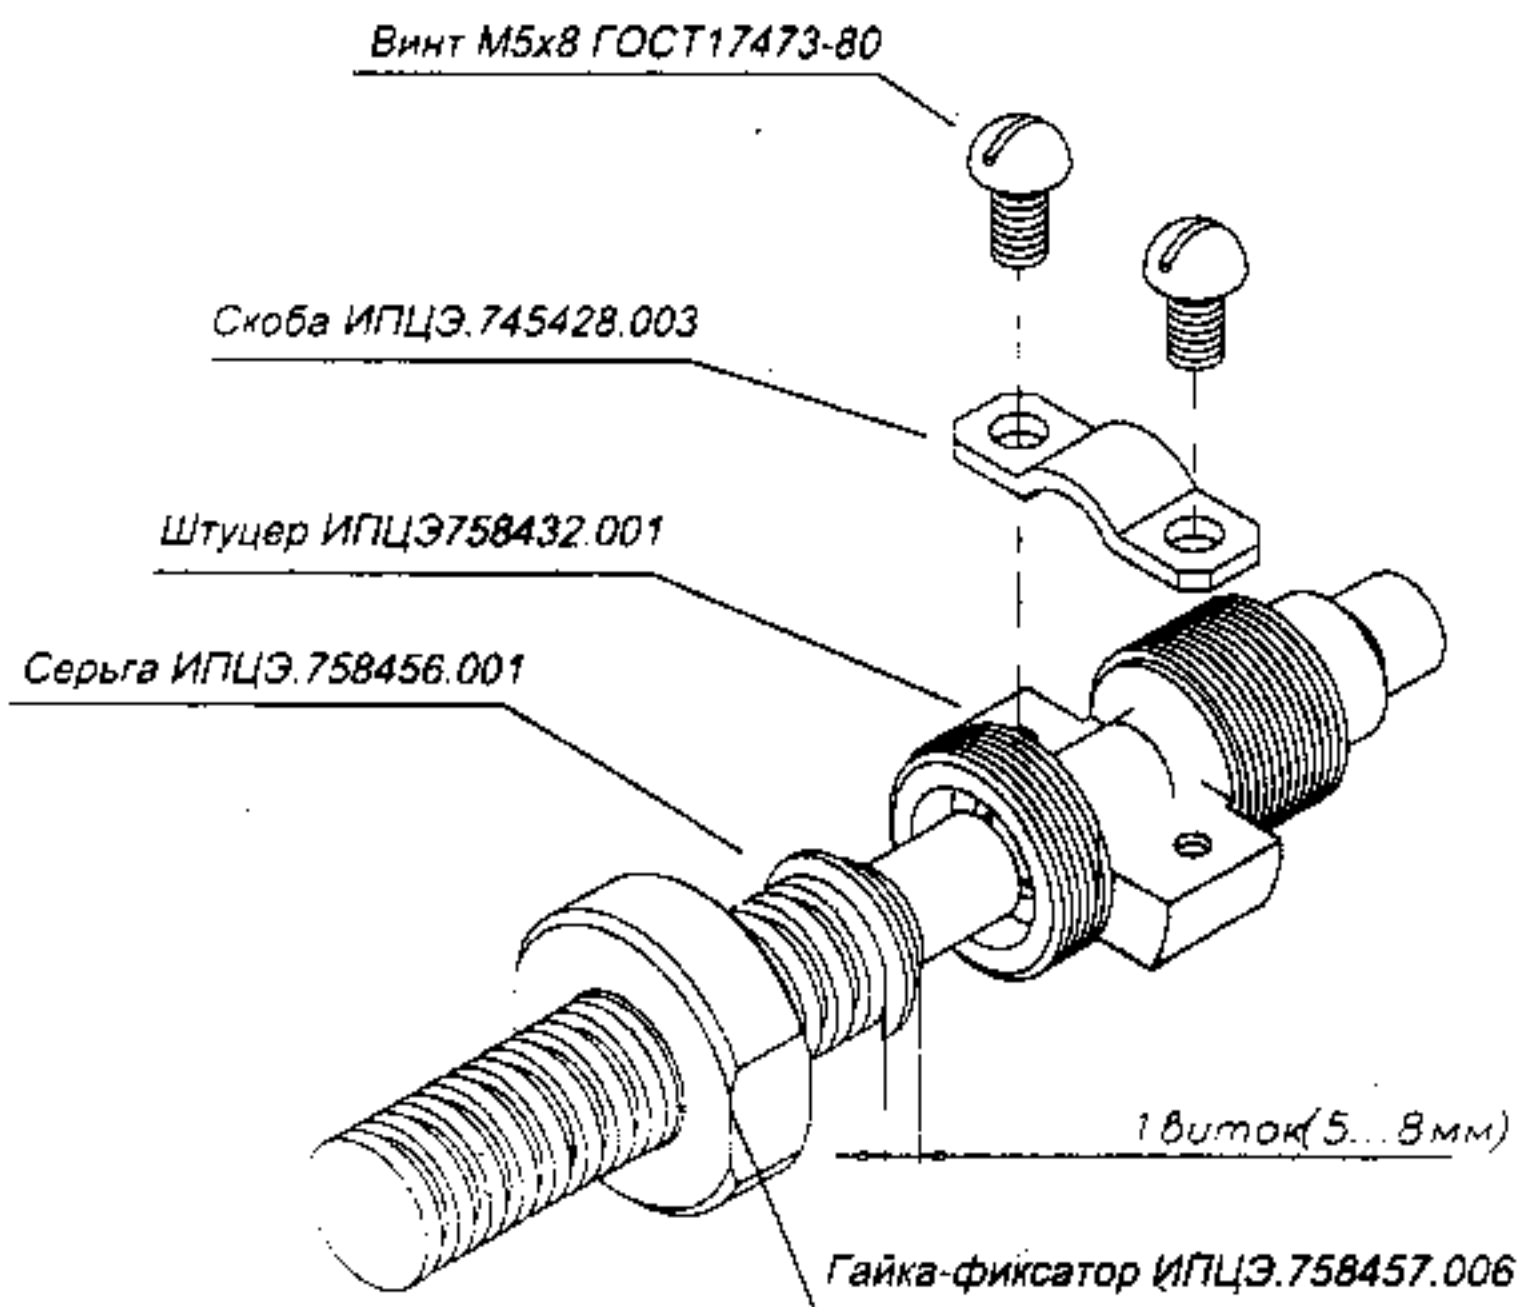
Монтаж кабеля КВВГ 4х1,5
